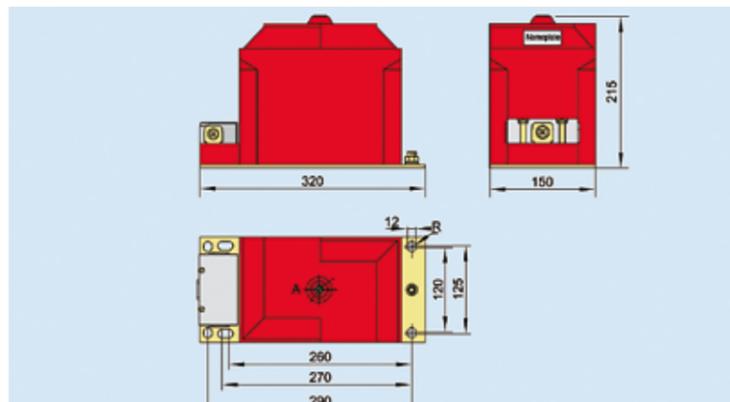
Внешний вид и размеры трансформатора напряжения JDZX10-10
